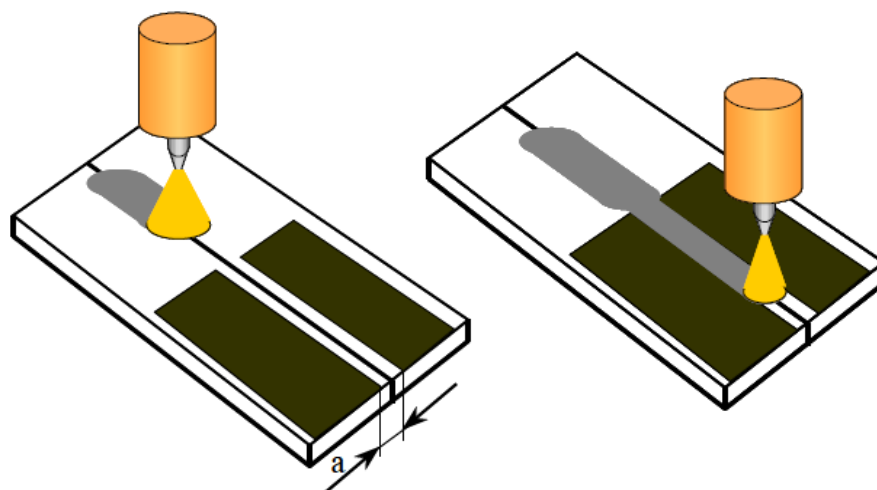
Técnica de soldagem caminho preparado de fluxo.
